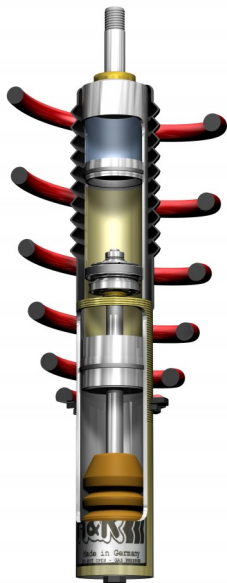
Anschlagpuffer (Abb. ähnlich)
